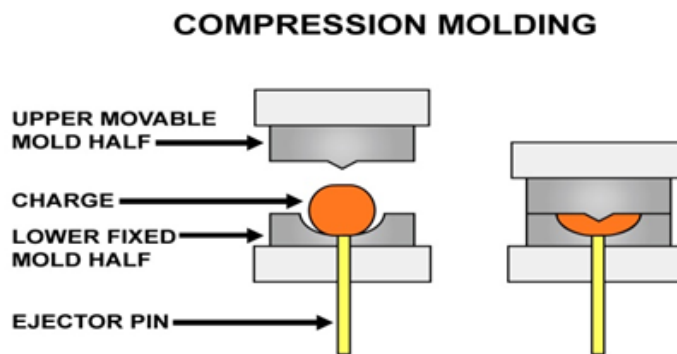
Moldeo por compresión (Moldex 3D, 2023)
